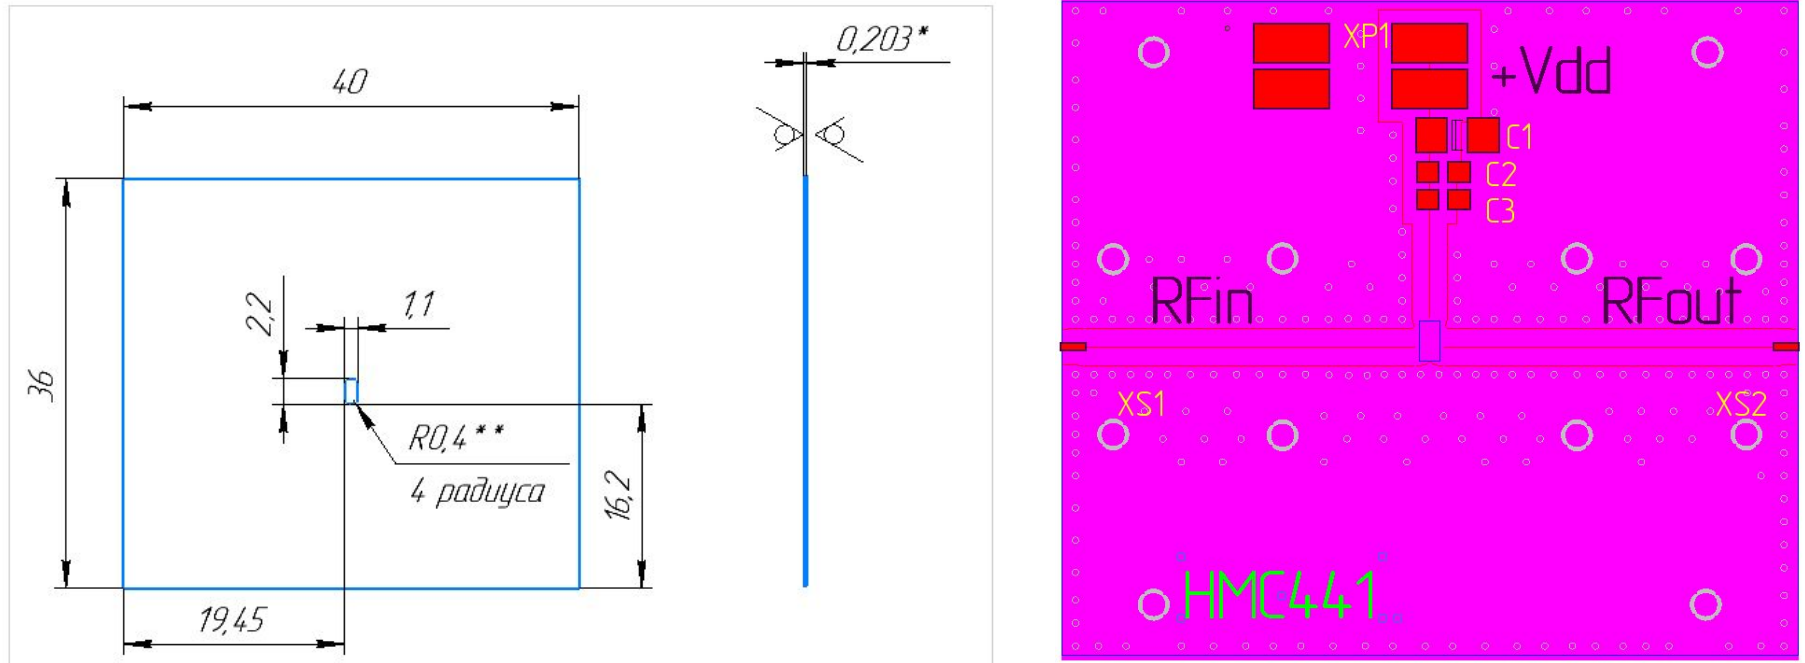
Печатная плата для подключающего устройства усилителя HMC441
